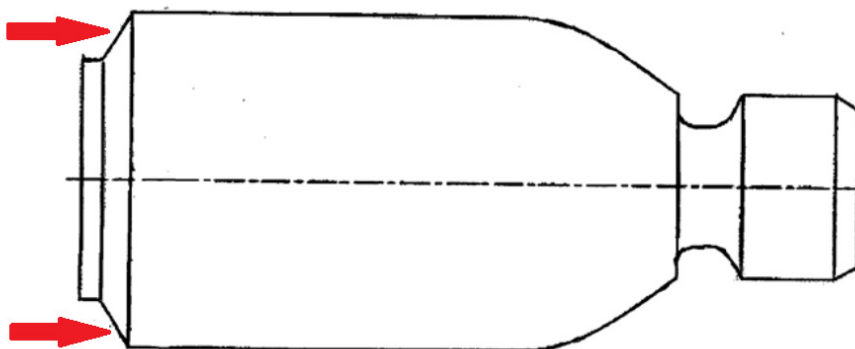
Representação do tampão terminal para solda por resistência e pressão, com indicação da região que será soldada
